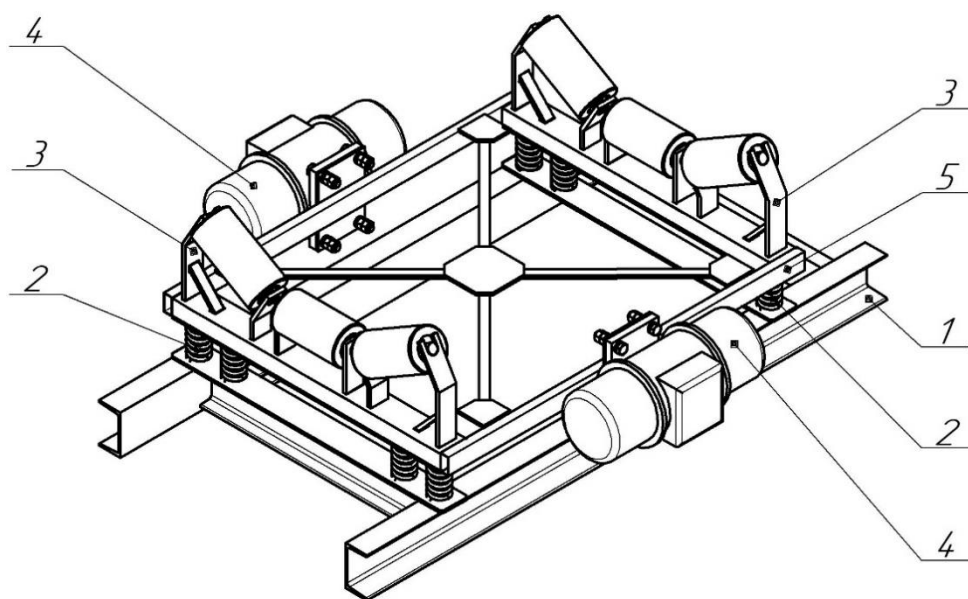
Вібруюча роликова опора стрічкового конвеєра
